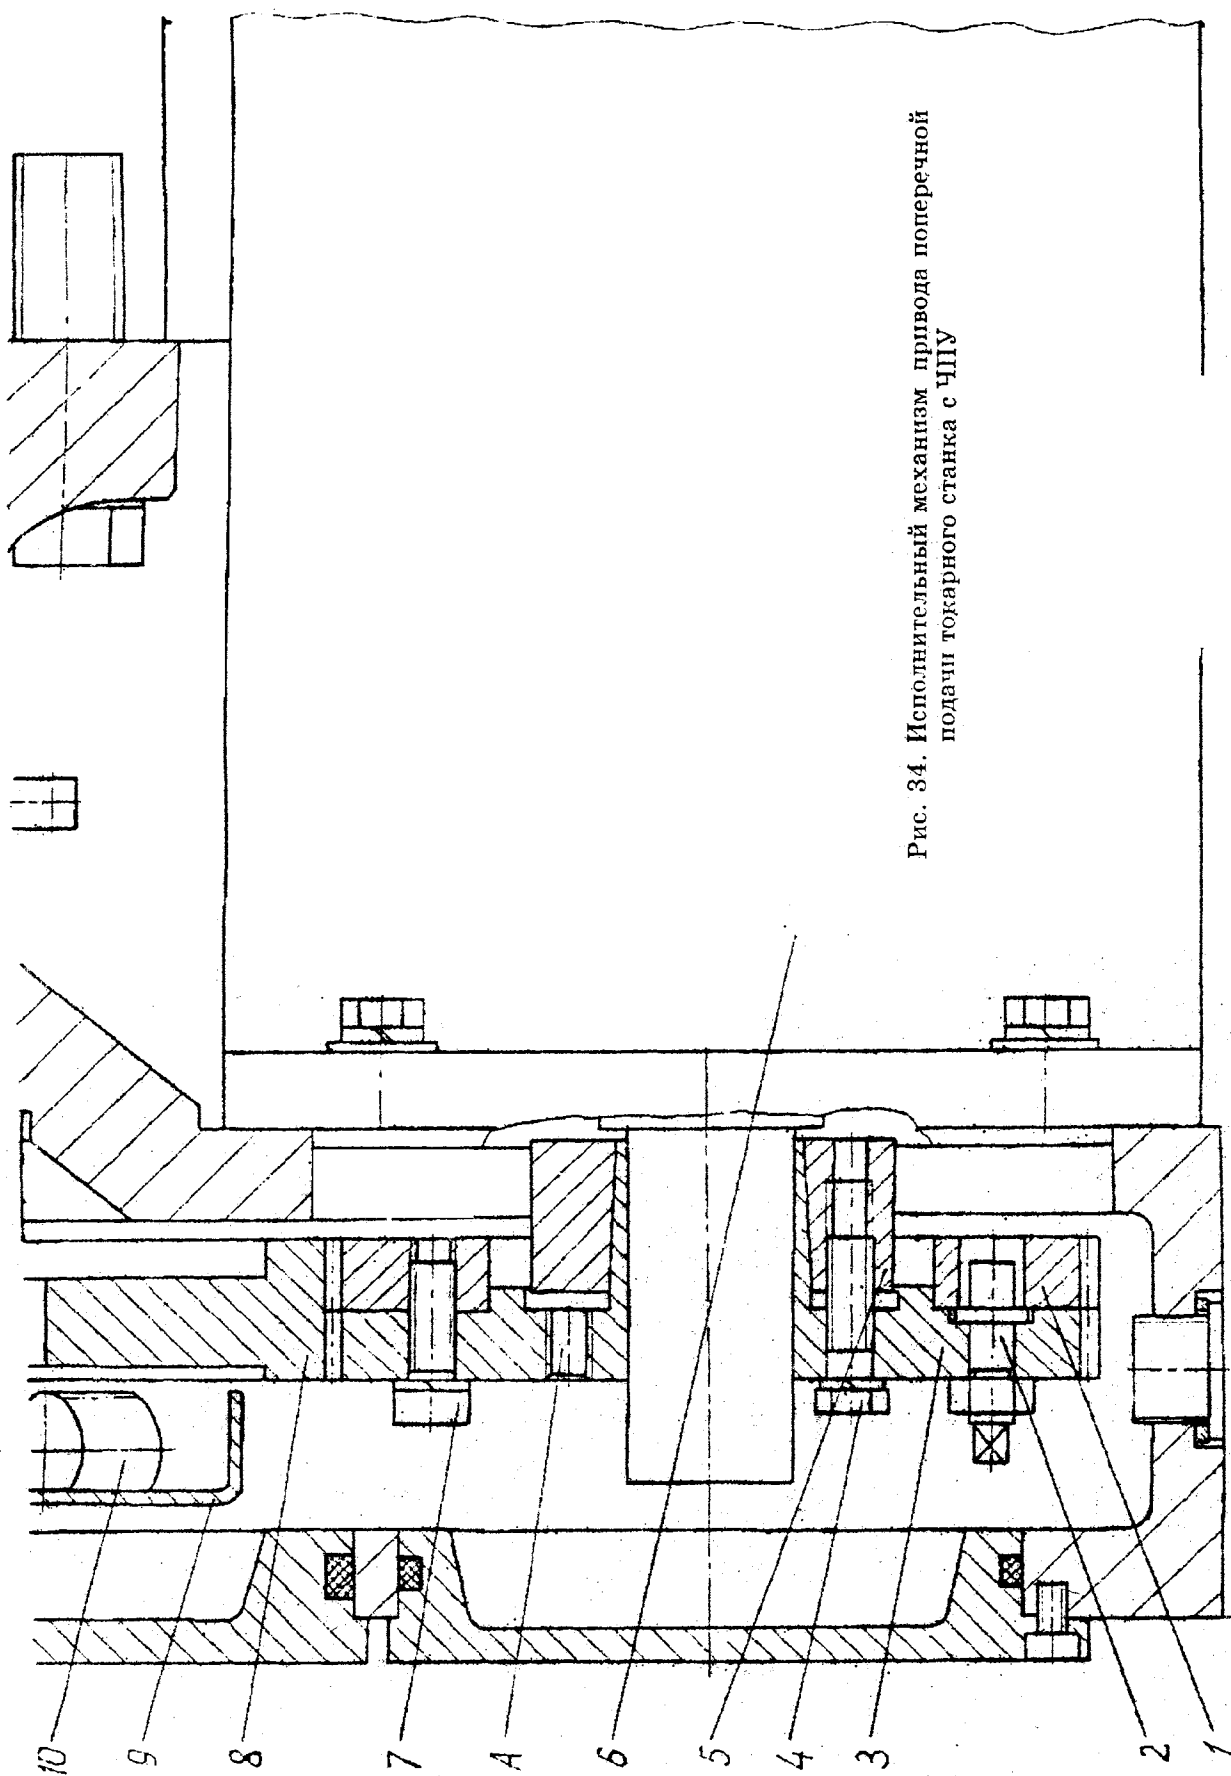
Исполнительный механизм привода поперечной подачи токарного станка с ЧПУ
